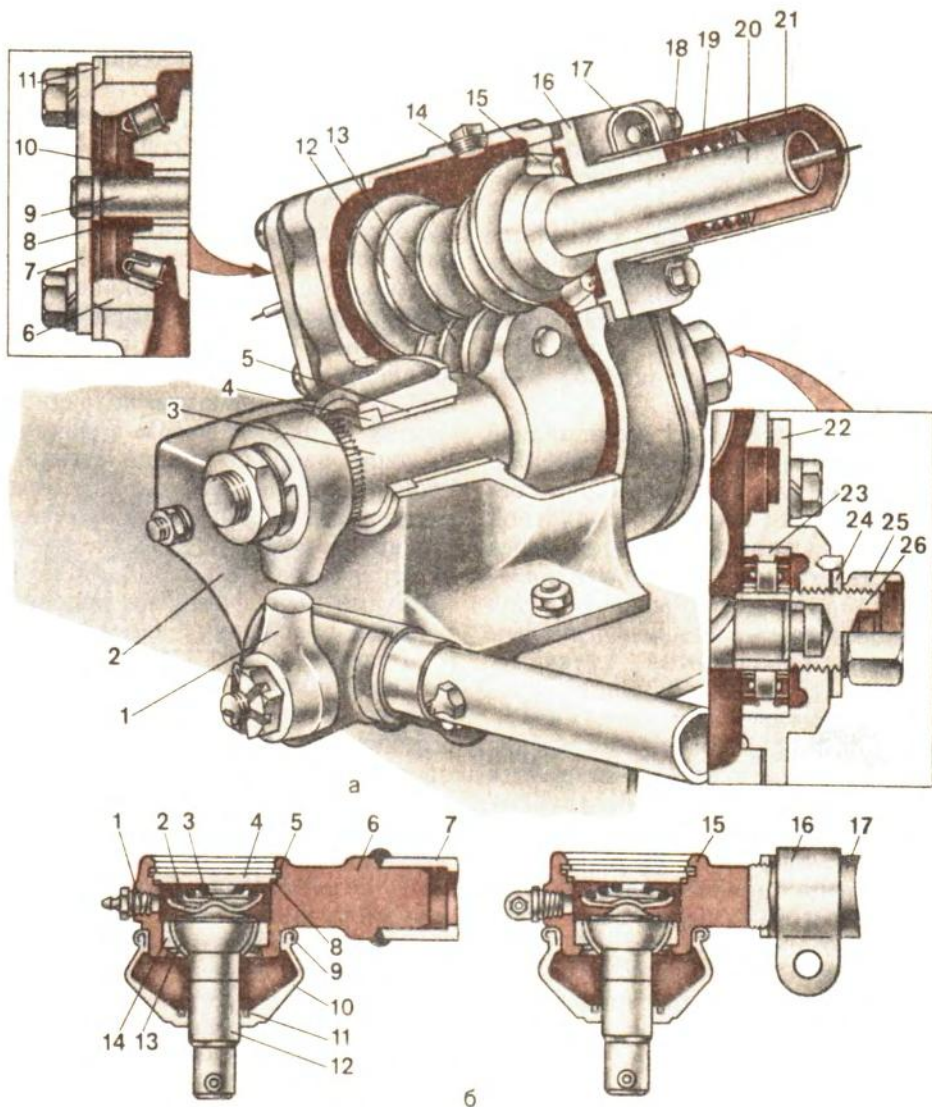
Рулевой механизм и шарнирные устройства автомобиля ГАЗ-53-12:
